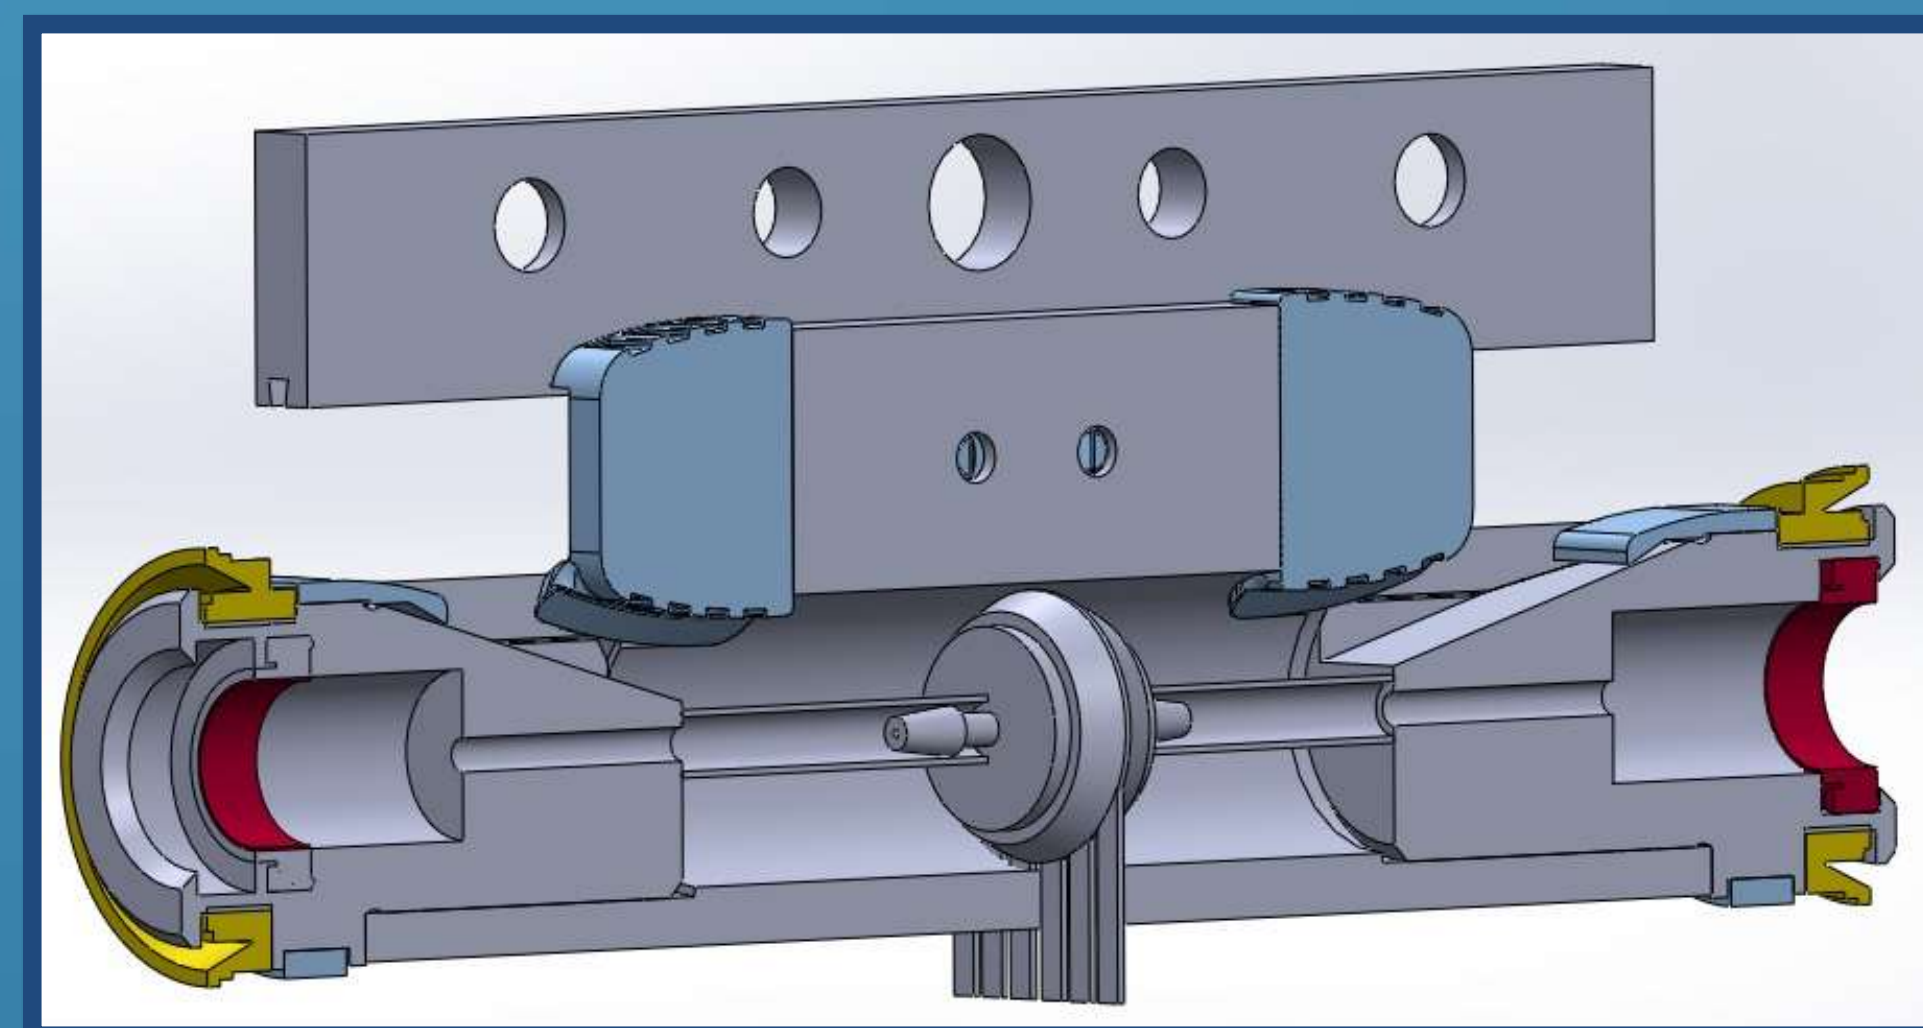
Representação em CAD do êmbolo com o sensor de pressão posicionado dentro.
